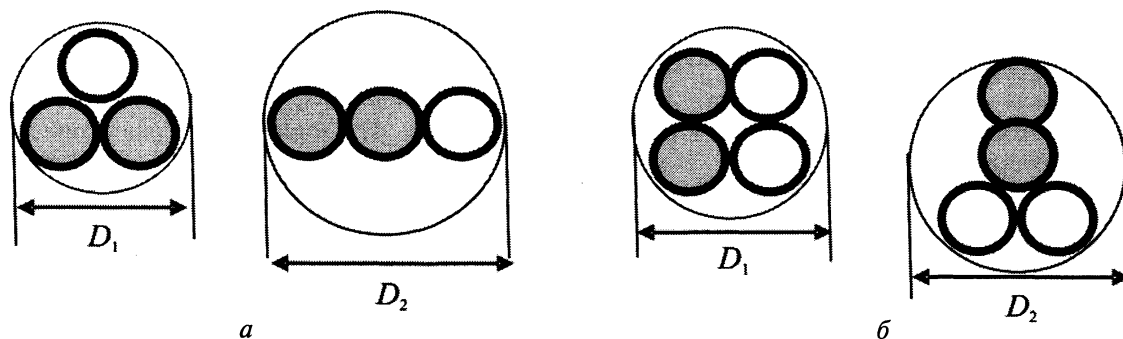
Однослойный металлокорд с переменной геометрией расположения проволок на шаге свивки: а – 2+1хd; б – 2+2хd
